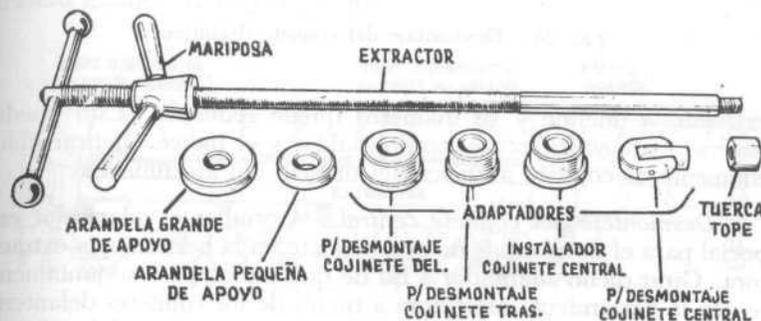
Herramienta especial extractora y colocadora de los cojinetes del árbol de levas.
